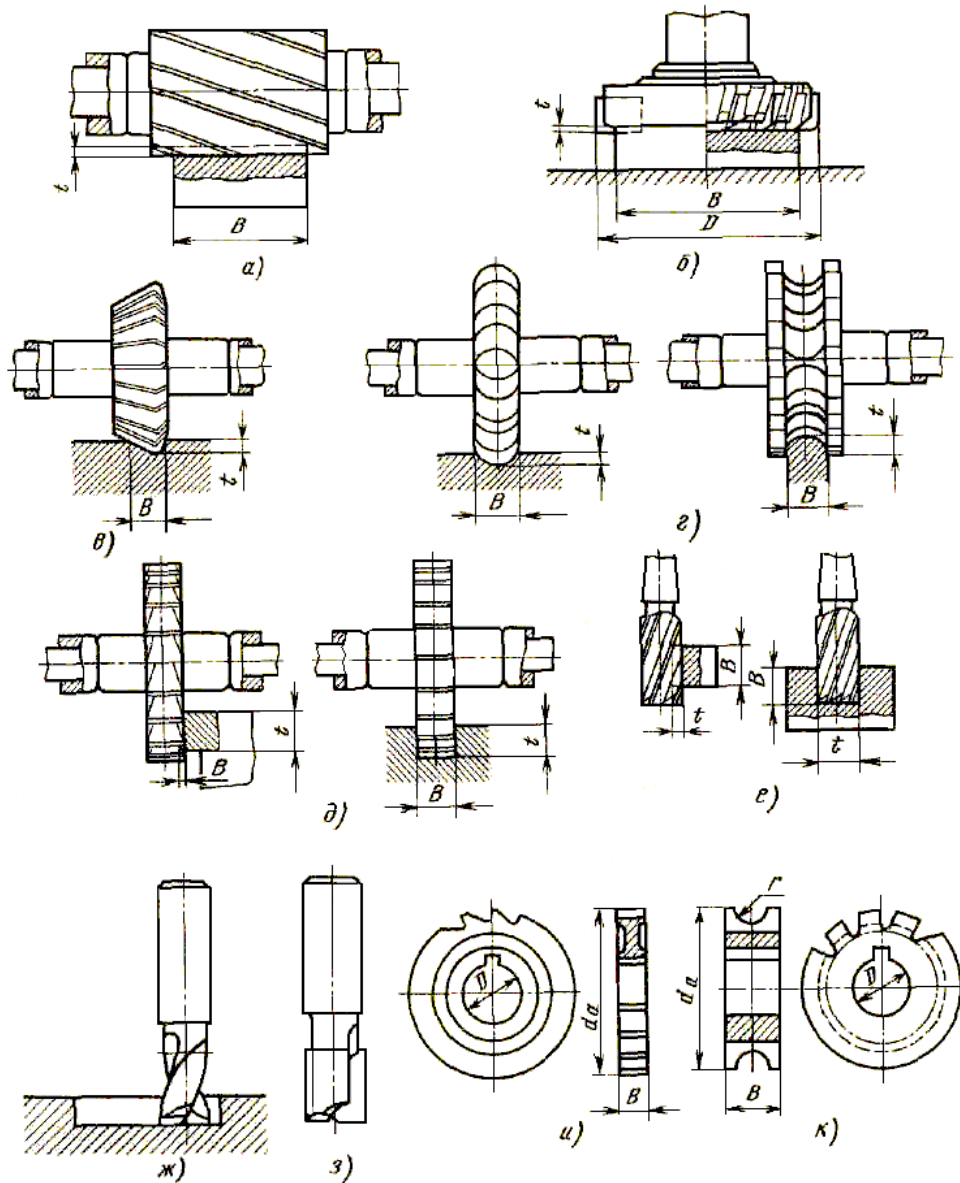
Типи фрез і оброблюваних поверхонь
